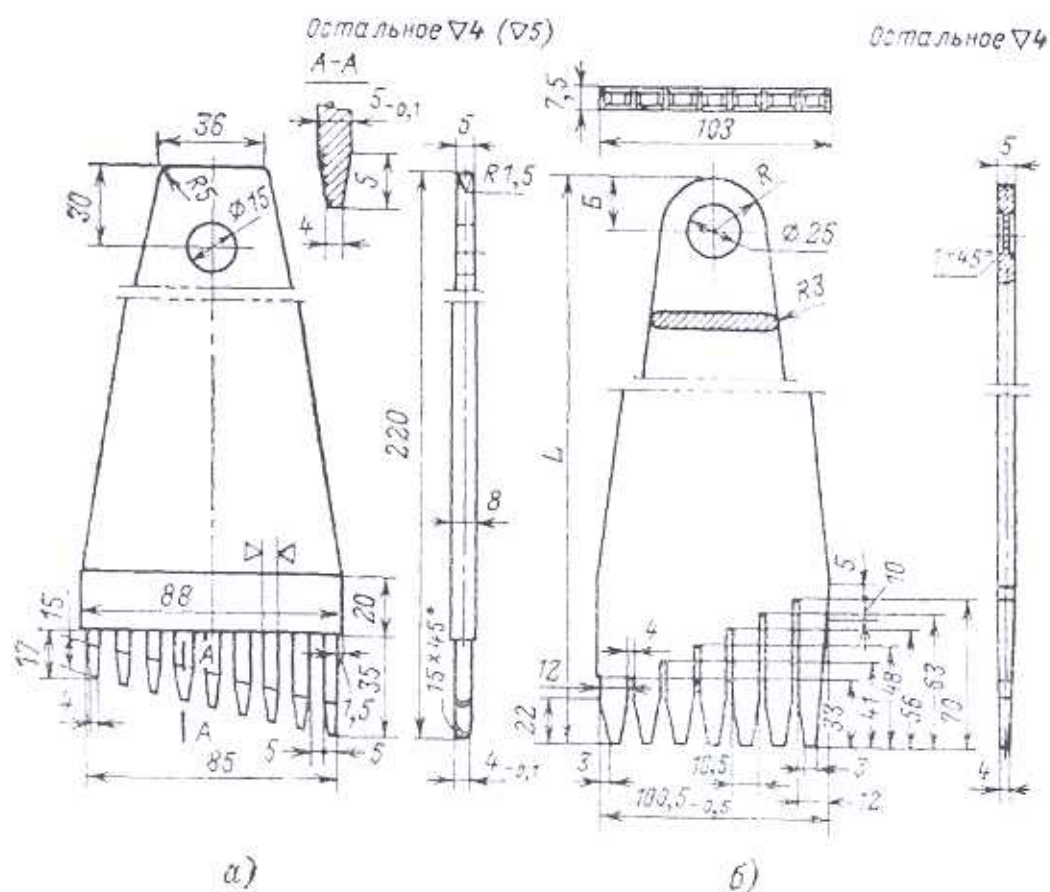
Гребенка для рихтовки трубок и установки колняков:
